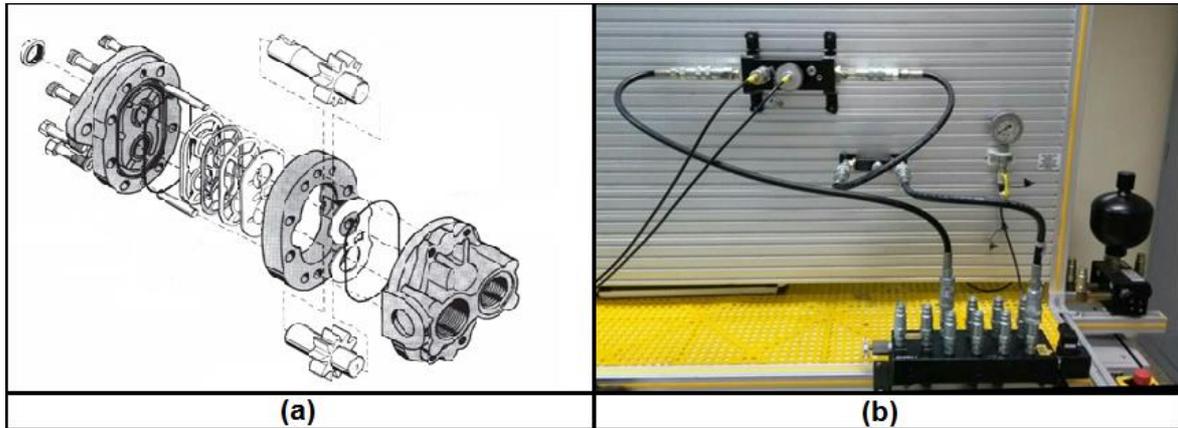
(a) Bomba de engrenagem / (b) Experimento realizado na bancada.
